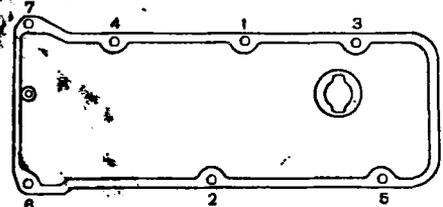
Порядок затягивания гаек крепления крышки головки цилиндров
